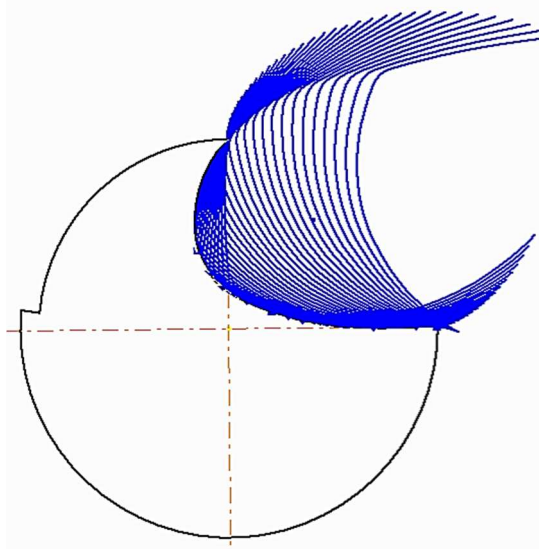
Торцевий переріз стружкової канавки свердла (отриманий)
